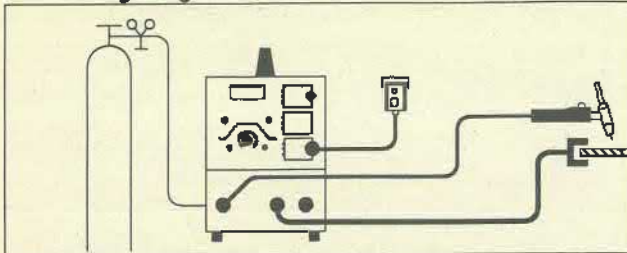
TRANSTIG 200 als WIG/TIG-Schweißgerät bestehend aus: Stromquelle, Schweißbrenner, Massekabel, Fernregler nach Wahl (TR 50-1, TR 51, TR 52-1, TP2)
